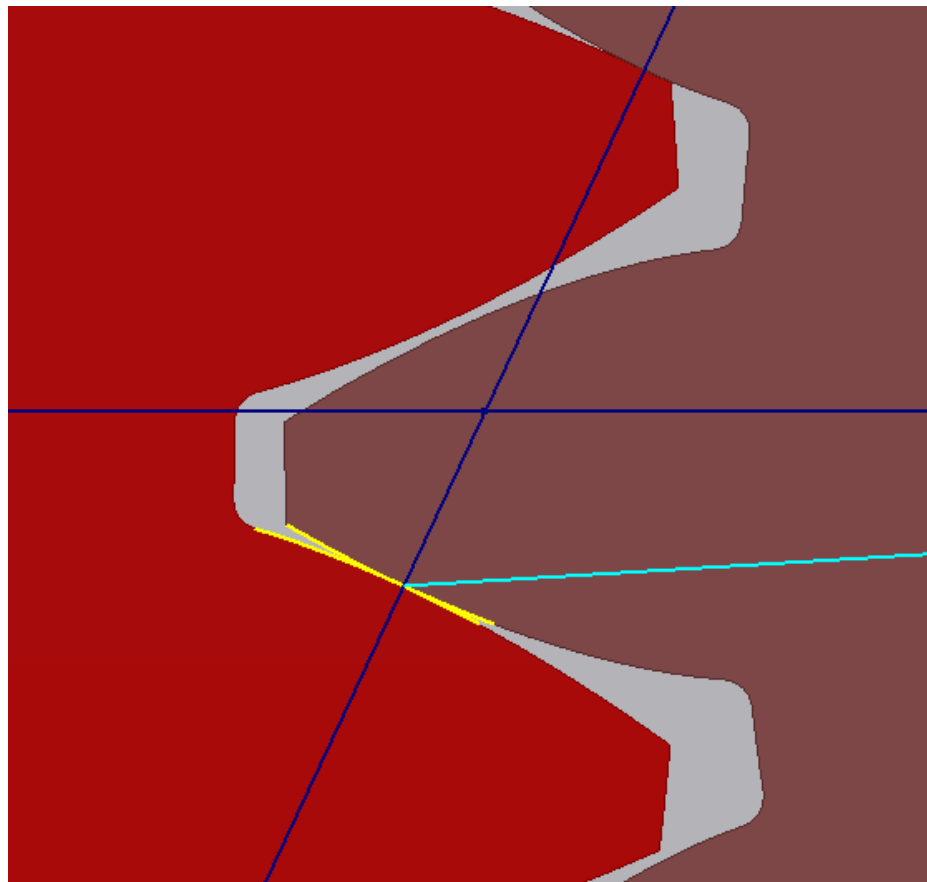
Flanco del diente en el engrane rojo en contacto tangencial con la cara del diente en el engrane café.
